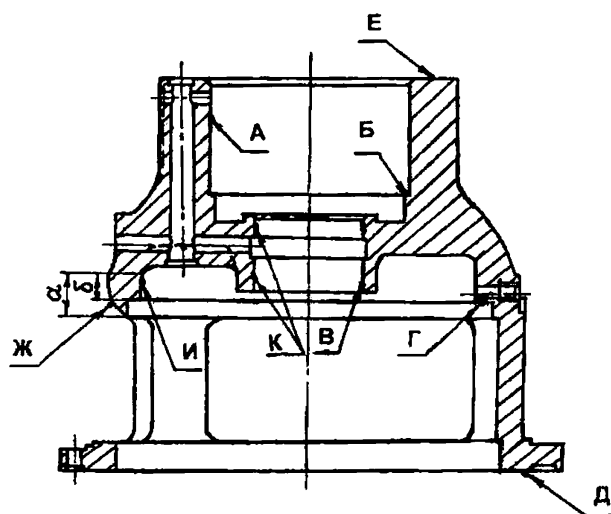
Корпус подшипника (поз. 3, рисунок 56)
